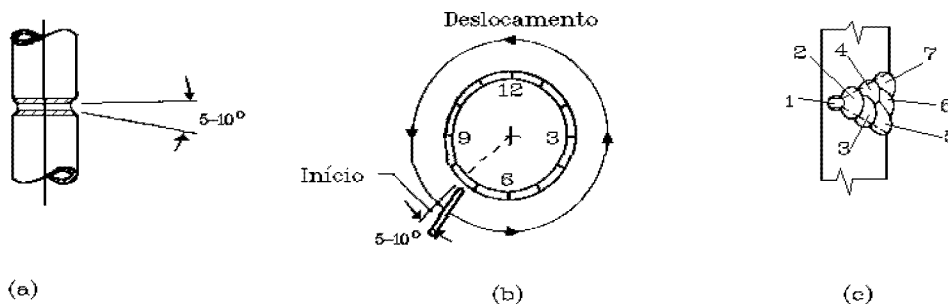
Soldagem de tubos na posição 2G: (a) Ângulo de trabalho; (b) Ângulo de deslocamento; (c) Seqüência de deposição.
